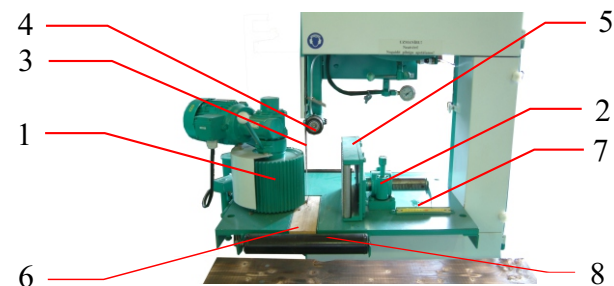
Механизм подачи материала (1-Валик подачи материала; 2-механизм регулировки размера; 3-пильная лента; 4-опорные ролики ленты; 5-блок опорных валиков; 6-деревянный вкладыш; 7-линейка; 8-опорный валик для пиломатериалов).
